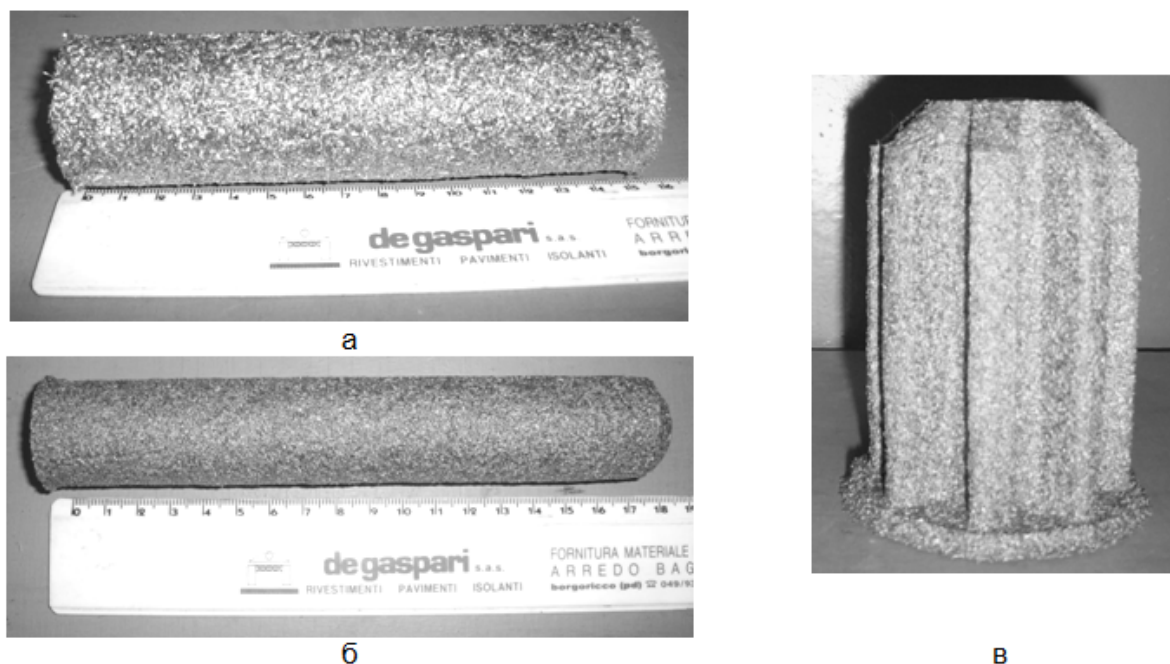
ФЭ, изготовленные методом сухого изостатического прессования: а – цилиндрической формы; б – цилиндрической формы с доньшком; в – цилиндрической формы с доньшком и ребристой поверхностью
